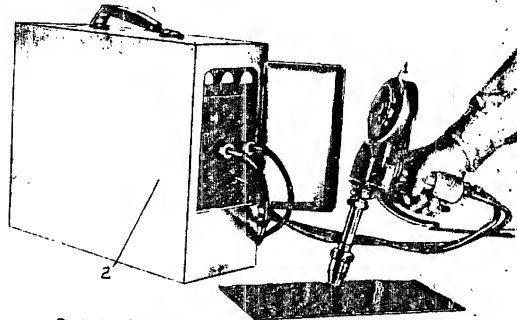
Сварочный полуавтомат типа ПГА-2м
